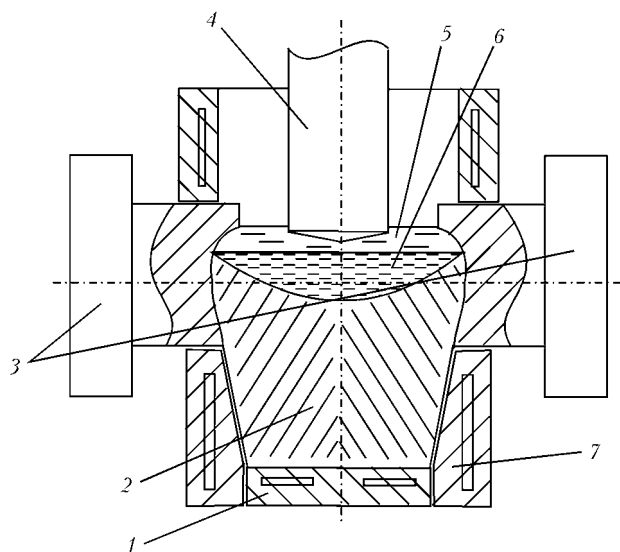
Схема ЭШЛП заготовки корпуса фланцевой задвижки: 1 — поддон; 2 — литая часть заготовки корпуса; 3 — приплавляемые патрубки; 4 — расходный электрод; 5 — шлаковая ванна; 6 — металлическая ванна; 7 — разборный кристаллизатор
